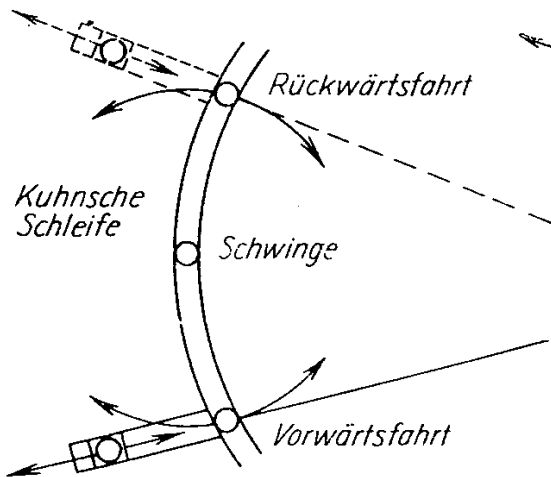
Steinspringen bei Aufhängung mit Kuhnscher Schleife
